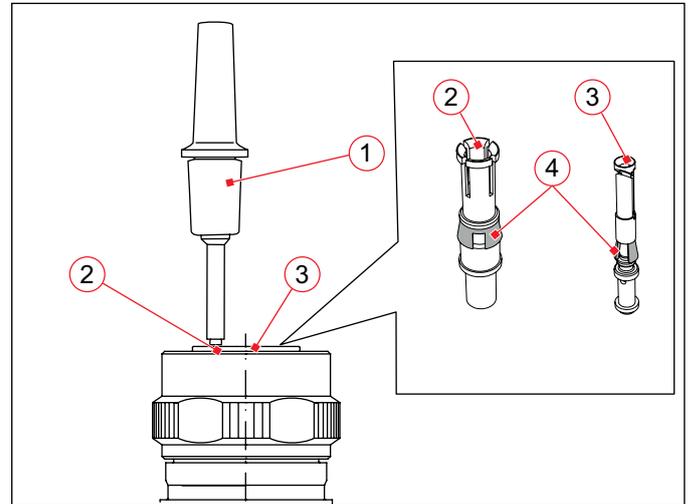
Demontage von Crimpkontakten (2,3) mit Ausdrückwerkzeug (1)
